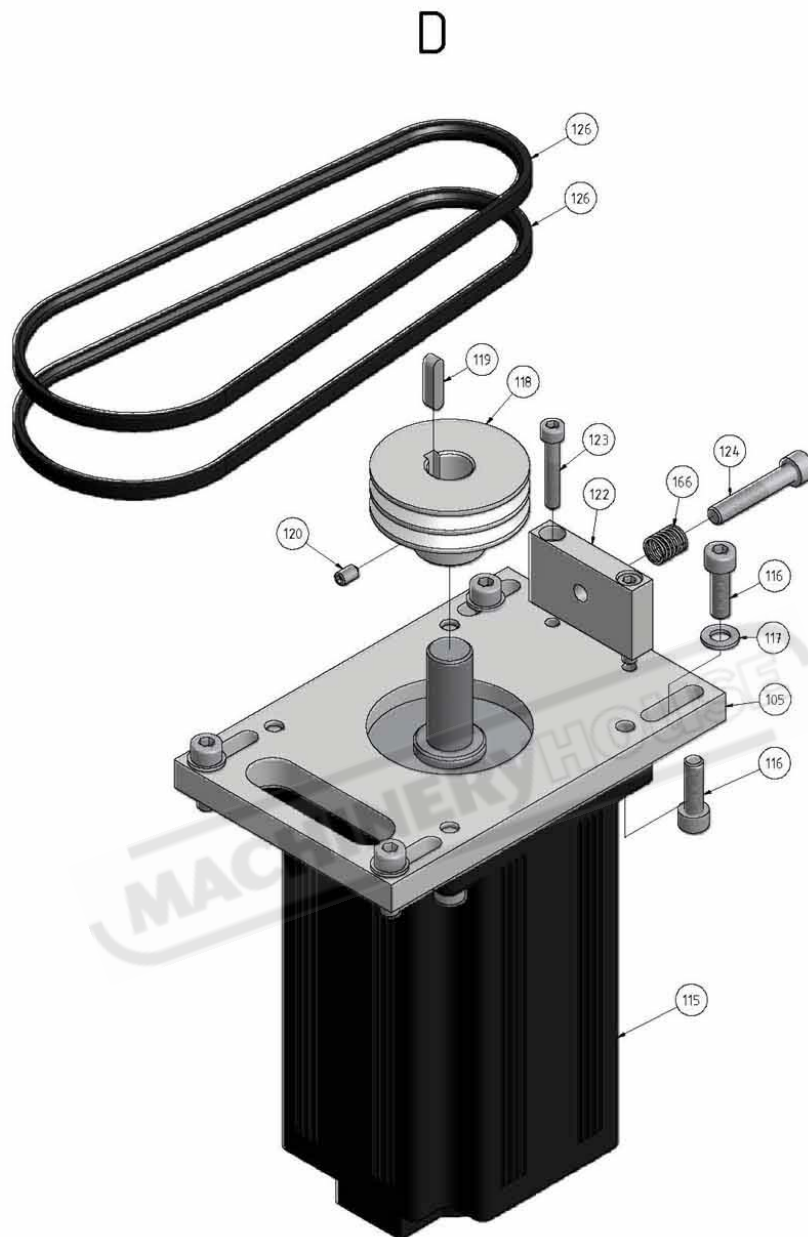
Bohrkopf 4 von 9 - Drilling head 4 of 9
